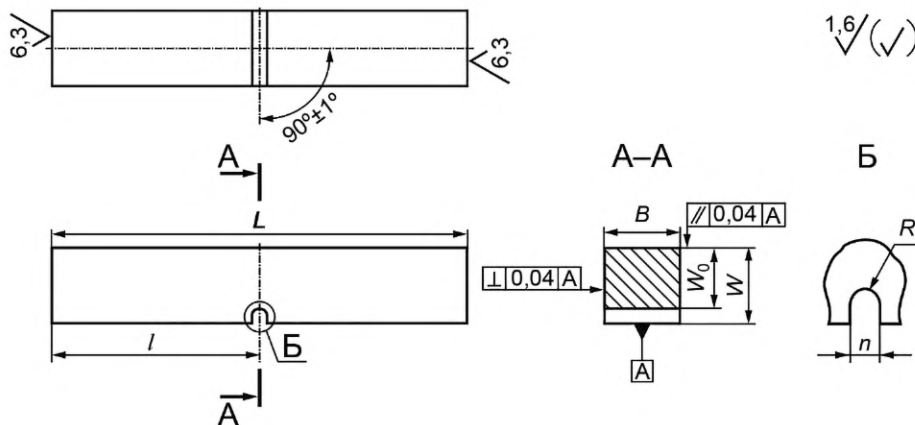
Эскиз стандартного образца Шарпи с U-образным надрезом
